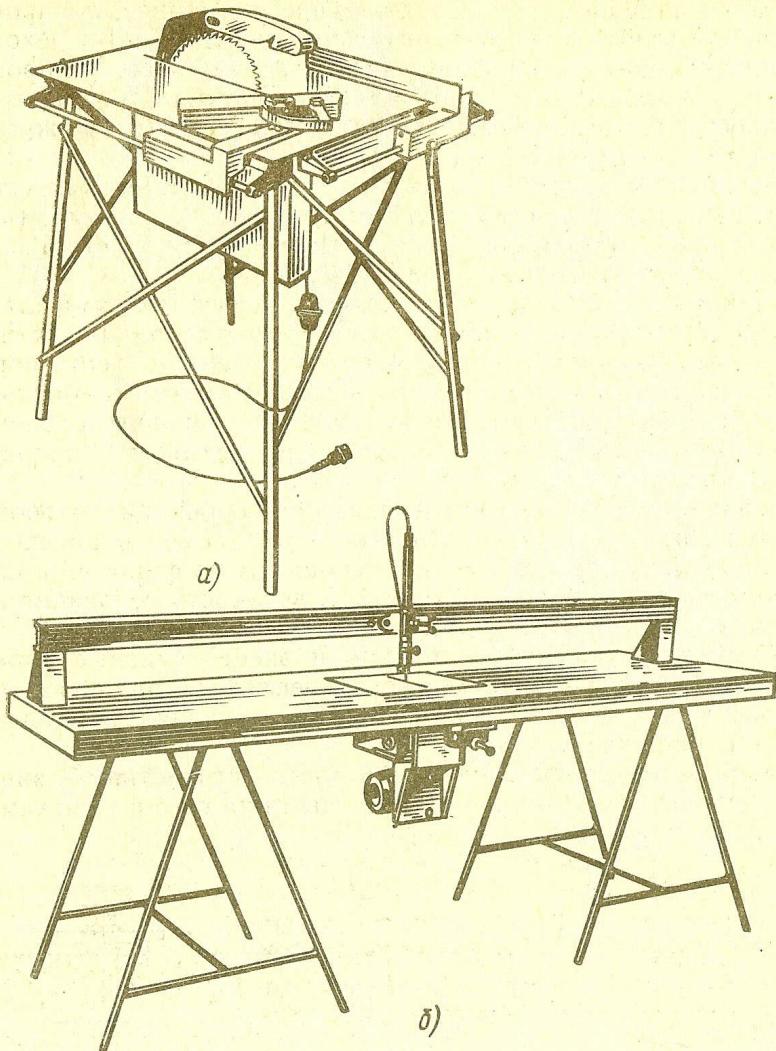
Нестандартные круглопильный (а) и лобзиковый (б) станки
